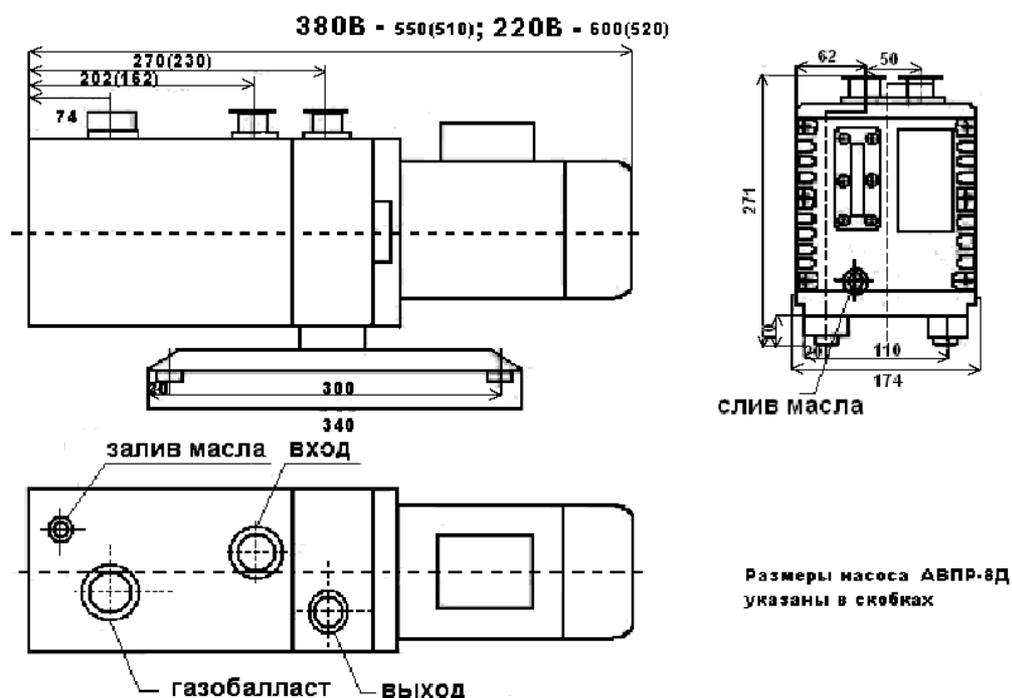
Габаритный чертеж насоса АВПР-8Д, АВПР-16Д
